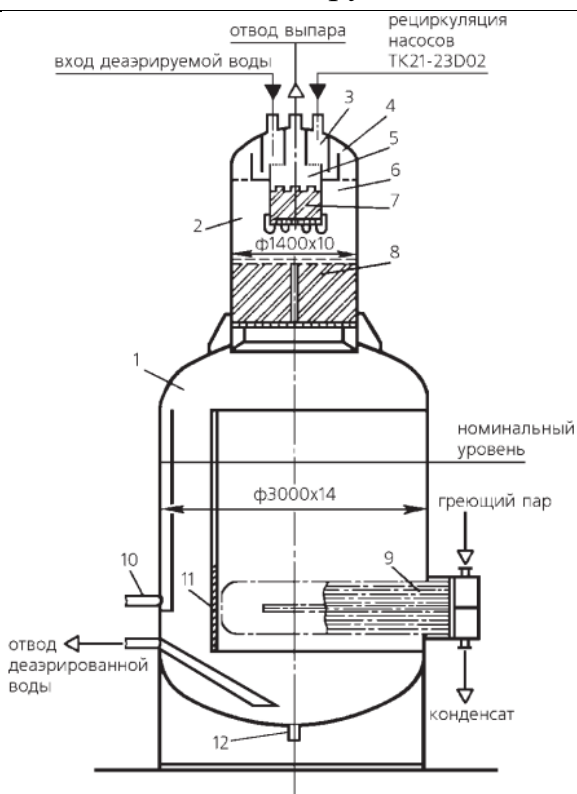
Конструкция деаэратора подпитки [2]:
